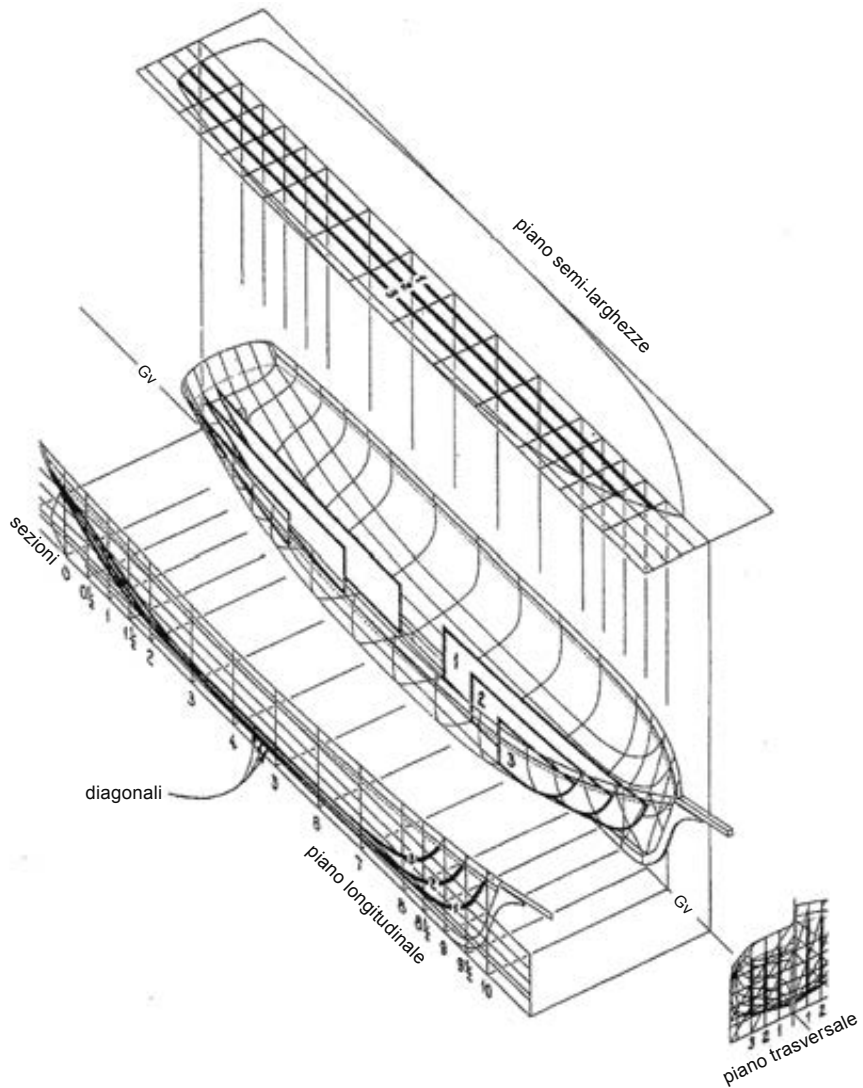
Vista delle sezioni longitudinali, riportate sul piano trasversale nelle due metà secondo la convenzione poppa a sinistra e prua a destra, come per le sezioni trasversali.
